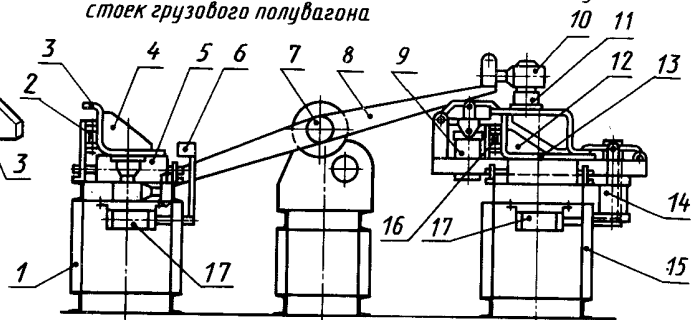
Автоматизированная установка для сборки угловой стойки грузового полувагона
